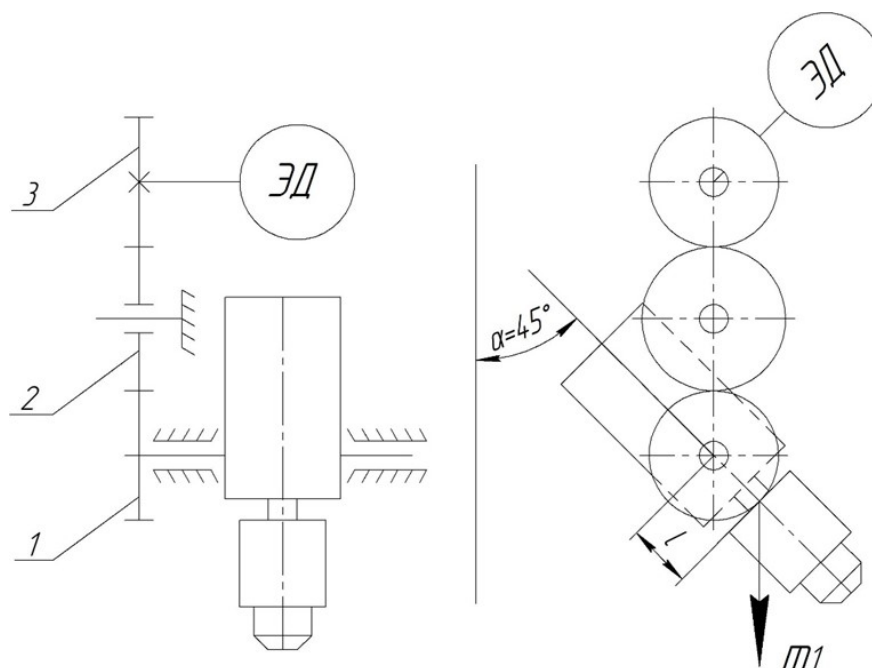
Расчётная схема поворотного механизма экструдера [8]
